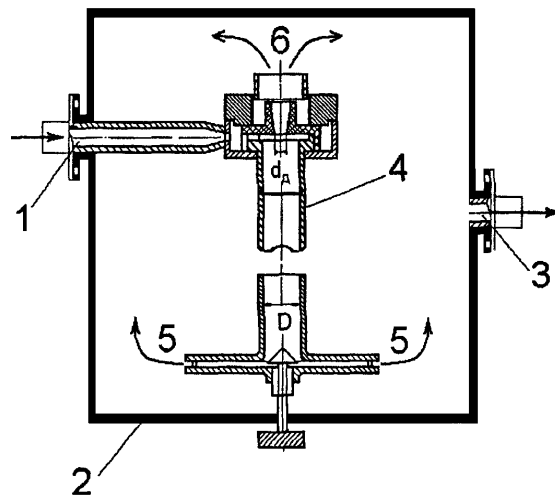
Устройство для снижения давления газа: 1 – патрубок подвода газа; 2 – корпус; 3 – патрубок отвода газа низкого давления; 4 – дроссель; 5 – патрубок «горячего» потока; 6 – патрубок «холодного» потока
